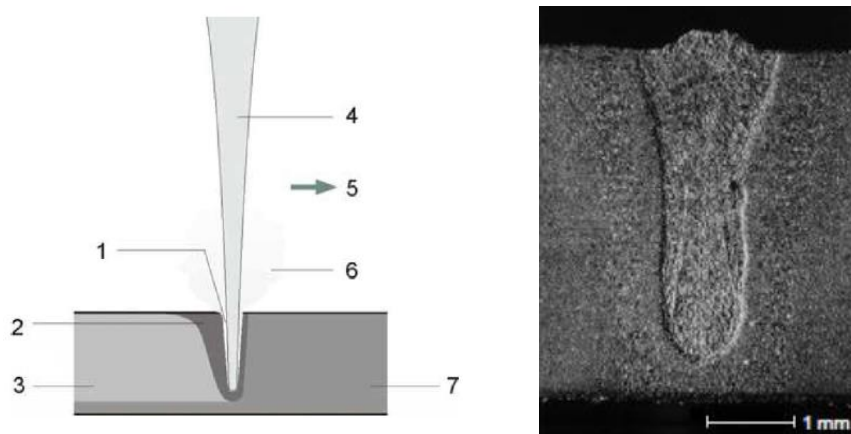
Princípio de Funcionamento da Soldadura por Penetração: 1 - Keyhole; 2 - Material Fundido; 3 - Cordão de Soldadura; 4 - Feixe *Laser*; 5 - Sentido de Avanço; 6 - Vapor de Metal; 7 - Peça a Soldar; (à esquerda) e Análise Microscópica de um Cordão de Soldadura Efetuado por Penetração (à direita) (adaptado de [63]).
